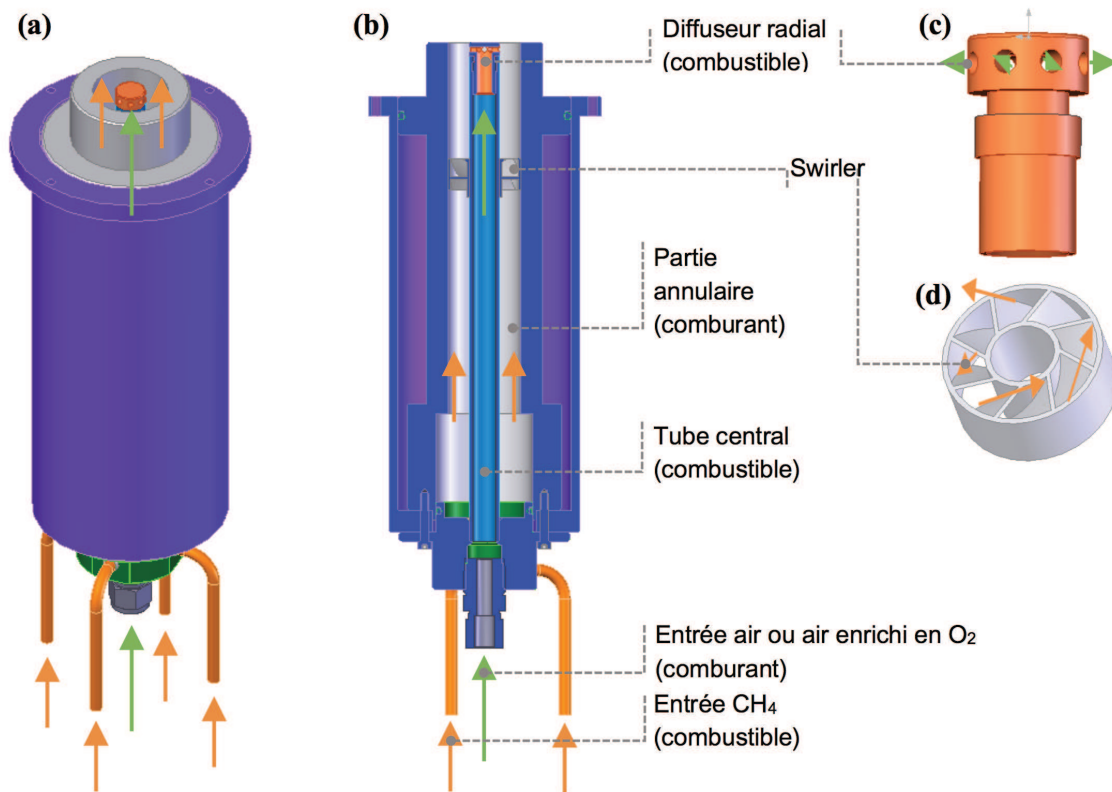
Représentation schématique de la chambre de combustion : (a) vue en perspective ; (b) vue en coupe.
